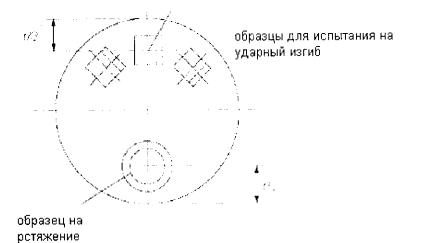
Расположение образцов. Пруток, поковка, отливка
